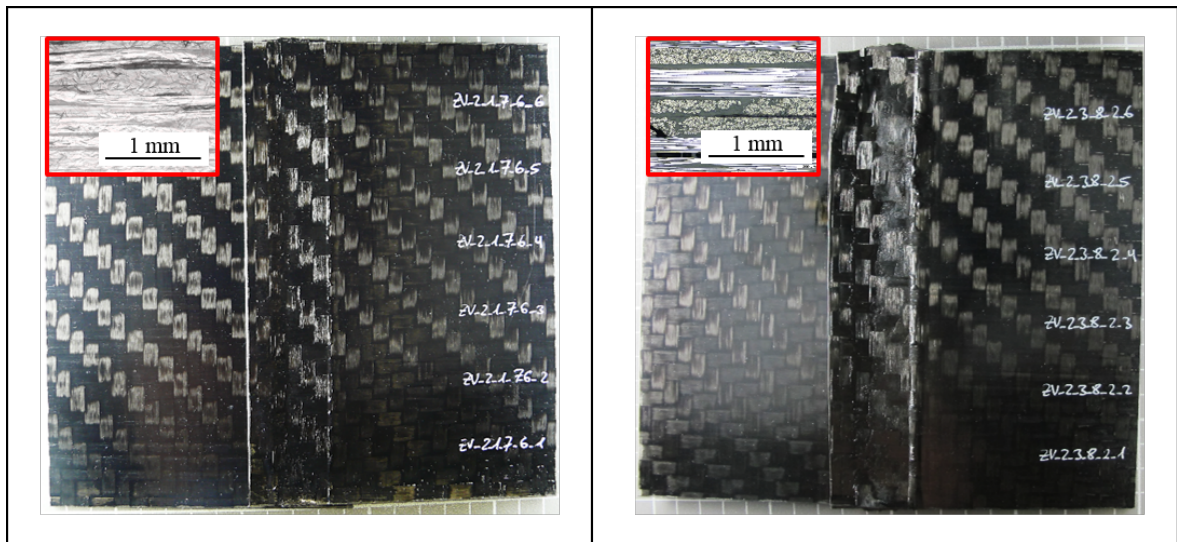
Schweißnaht der Versuchsreihen KR-01 mit Rollendurchmesser  $D=40$  mm (li.) und Versuchsreihe KR-02 mit Rollendurchmesser  $D=80$  mm (re.).
